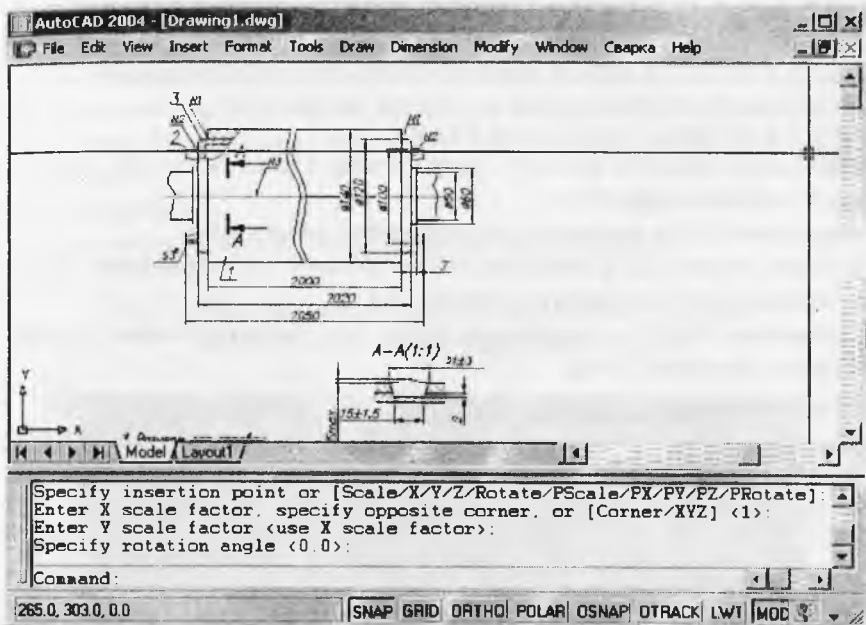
Блок сварной сборочной единицы вставлен в текущий чертеж
